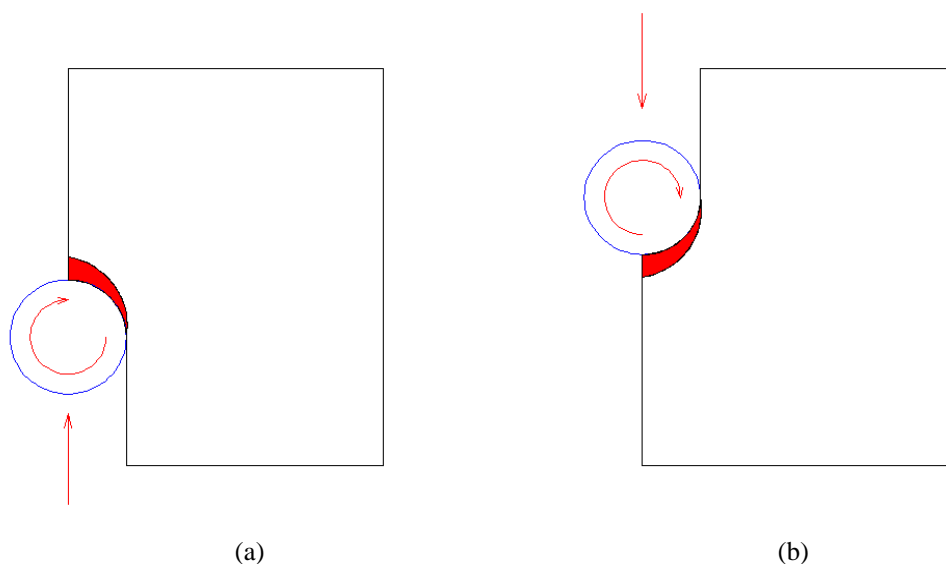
Contorno exterior: Maquinagem Concordante (a); Maquinagem Discordante (b).
